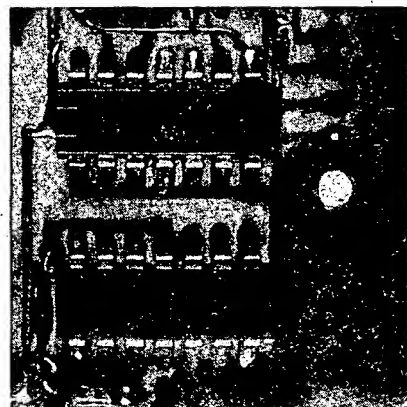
Tvar spojů a rozložení součástí generátoru z obr. 96
